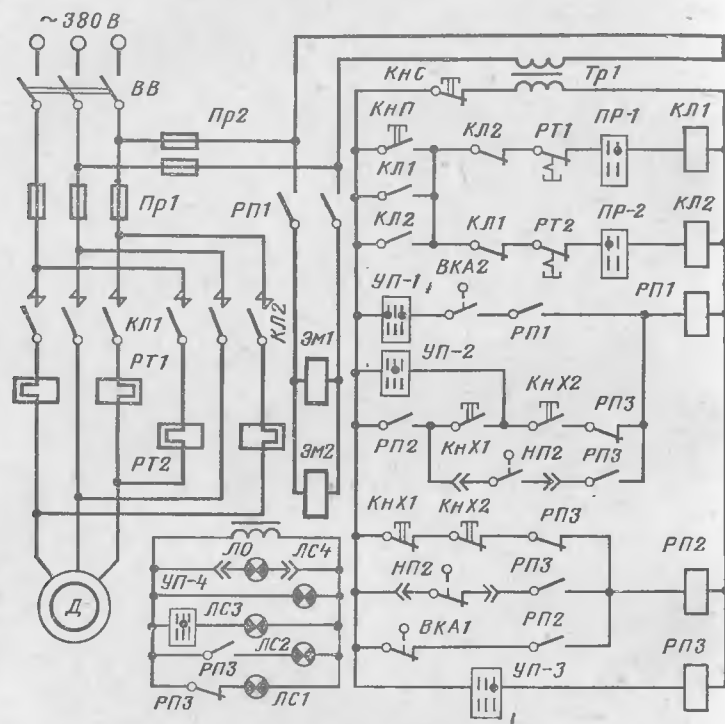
Электрическая схема кривошипного ковочно-штамповочного пресса.
